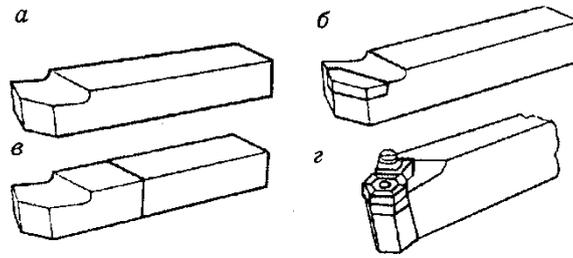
Типы токарных резцов по конструкции: цельные (а, б) составные с припаянными (в) или с механическим креплением (г) пластинами
